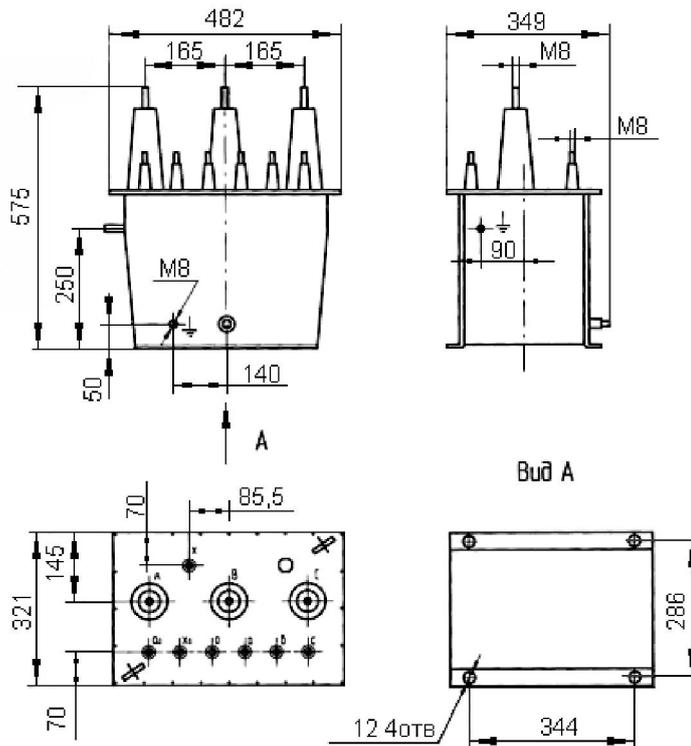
Габаритные размеры трансформатора НАМИ
